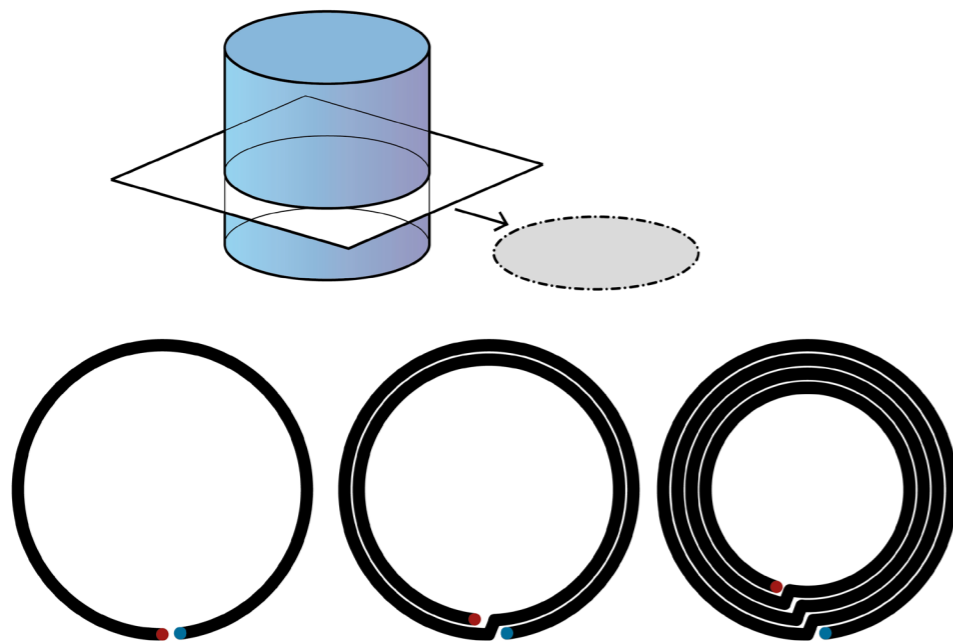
Effetto dell'altezza layer rispetto alla dimensione dell'ugello. Fonte: +LAB.
